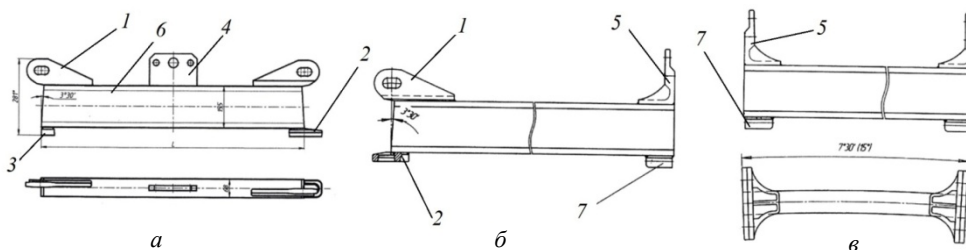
Сегменты монорельсового пути: а – ходовой; б – соединительный; в – поворотный; 1 – проушина; 2 – замок; 3 – ключ; 4, 5 – фланцы; 6 – балка; 7 – петля
